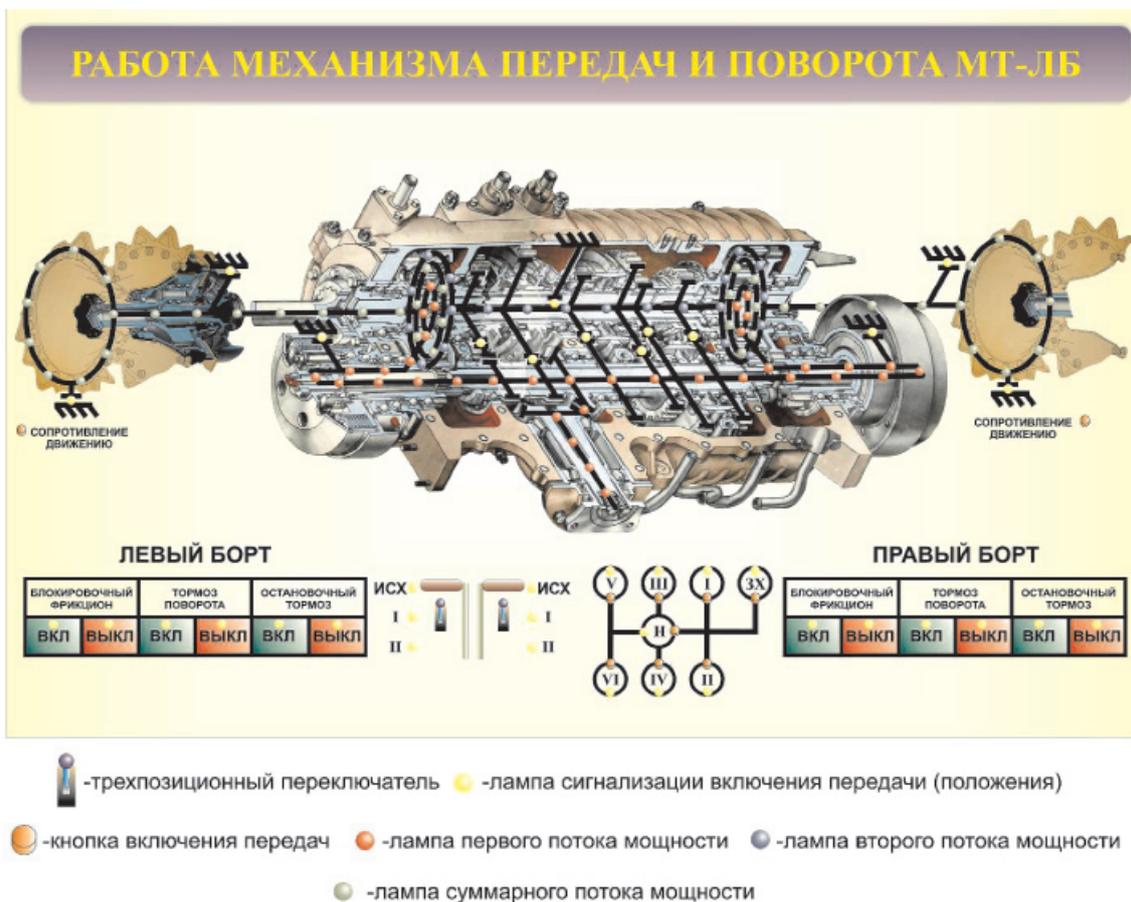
Внешний вид стенда «Работа механизма передач и поворота МТ-ЛБ»
